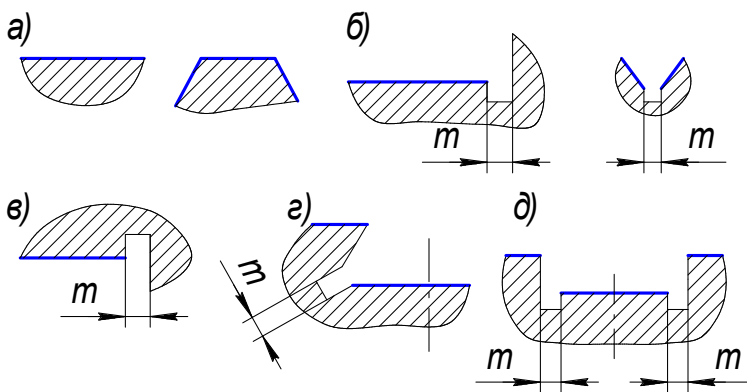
Типи поверхонь оброблюваних торцевими фрезами
